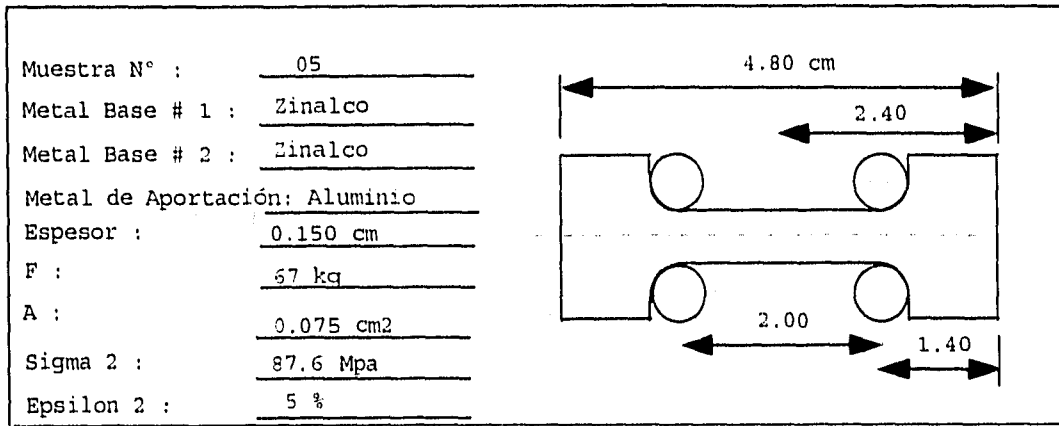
Probeta No.5, valores de prueba a la tensión para soldadura realizada entre Zinalco y Zinalco con material de Aporte Zinalco.
